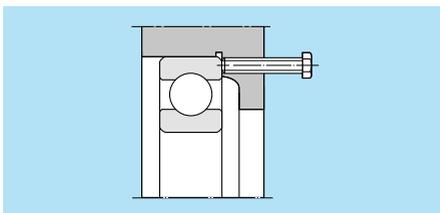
Gewindeschraube zum Ausdrücken des Außenringes
